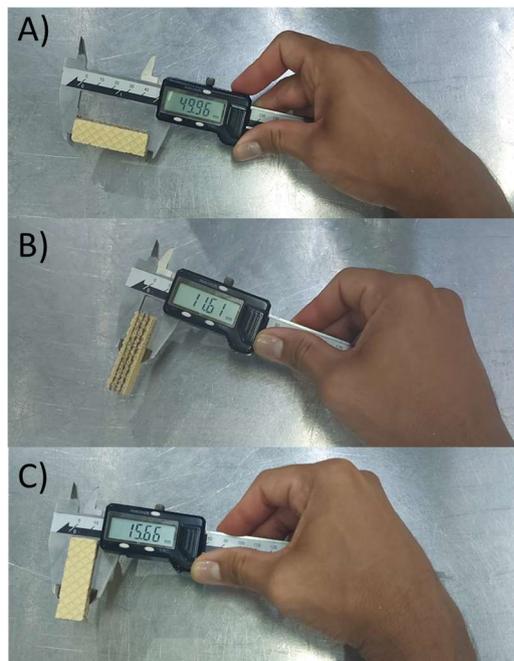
Demonstrativo do processo de medição do dimensional do produto – Imagem A) Comprimento, B) Altura, C) Largura
